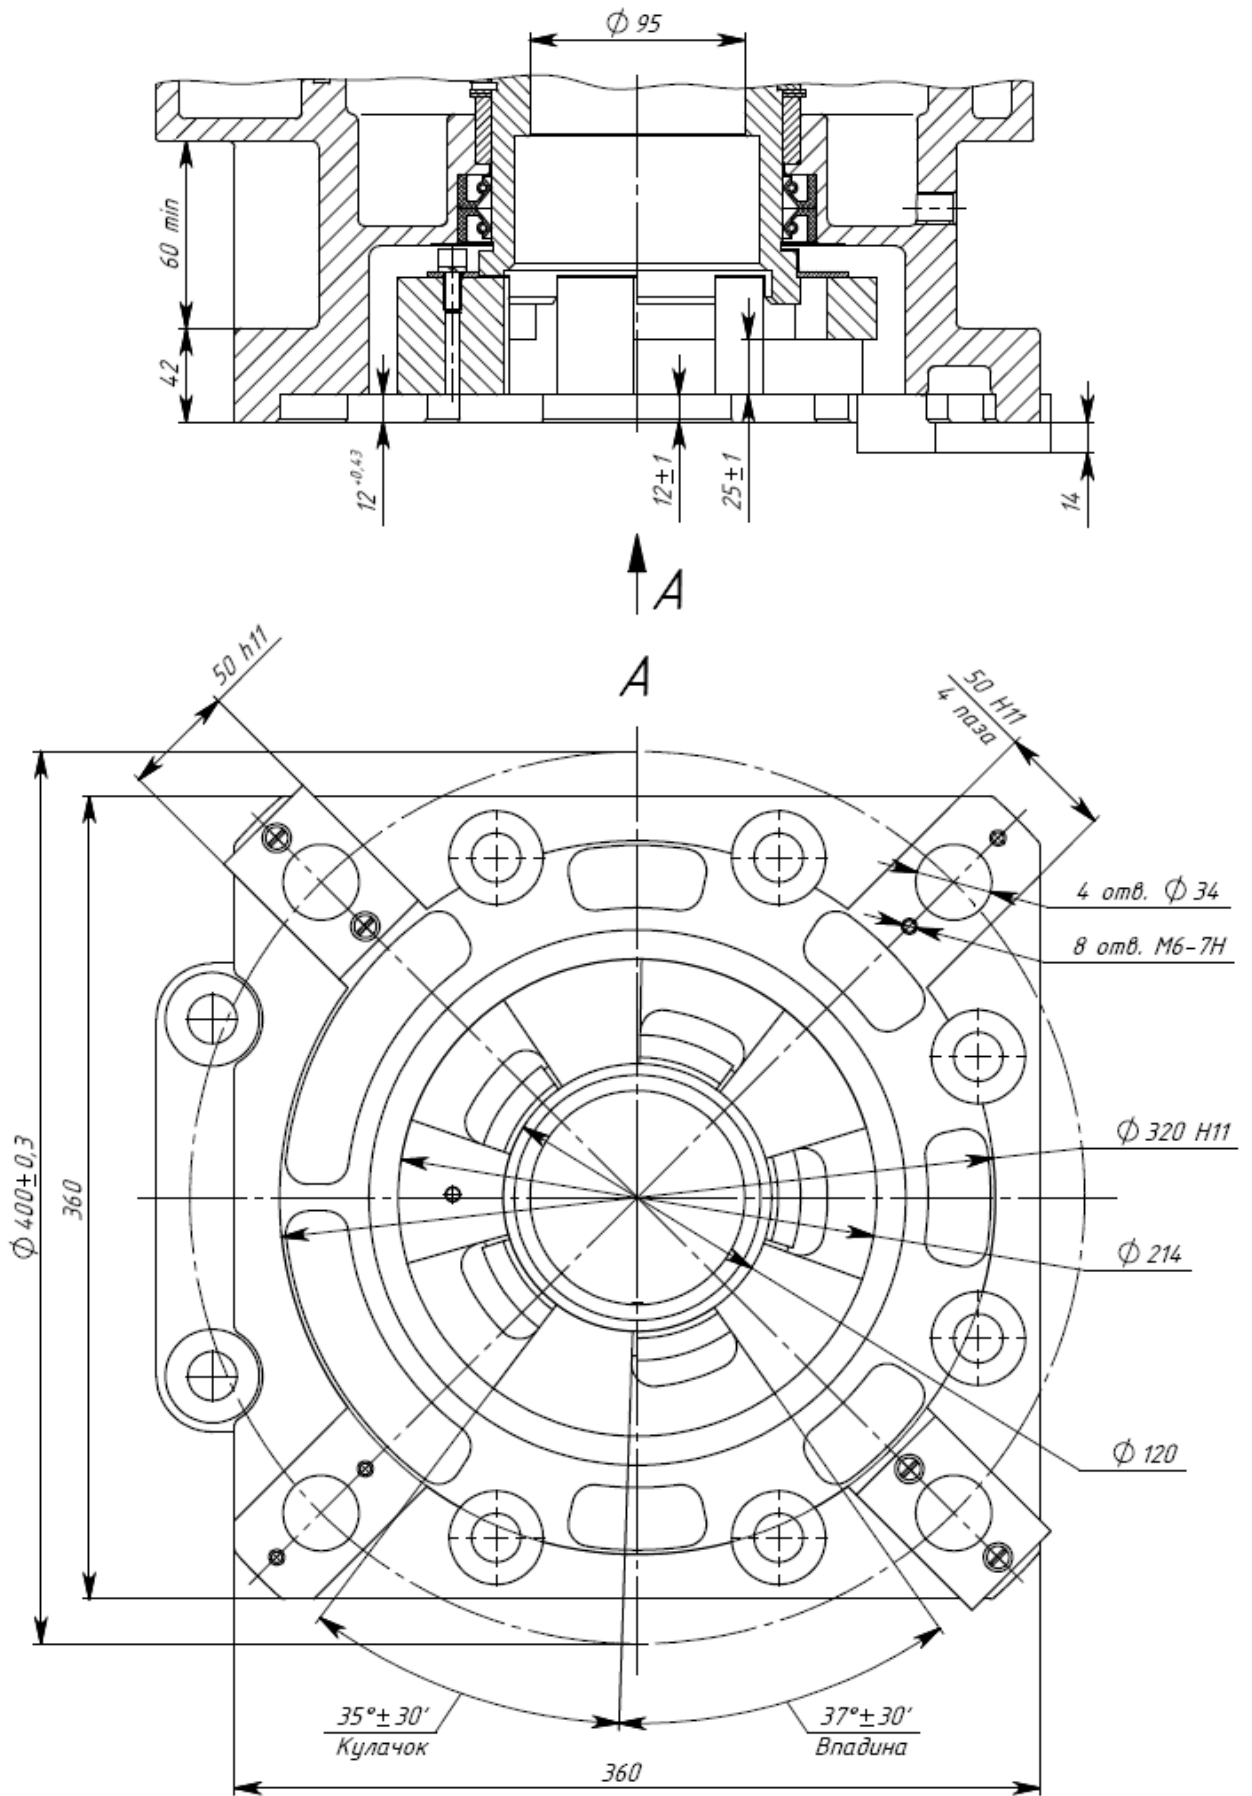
Присоединение типа Д для конструктивной схемы 43
